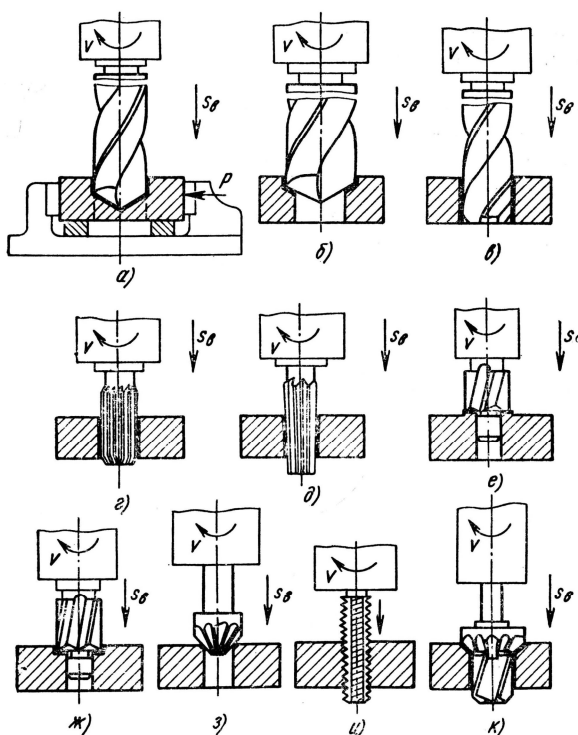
Схеми обробки заготовок на вертикально-свердильних верстатах
